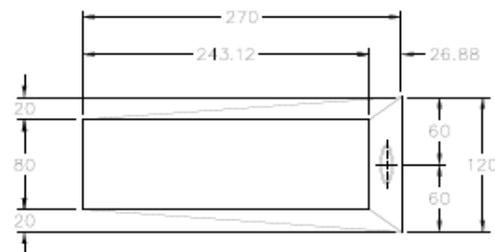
Vista E-E. Detalle geométrico de rebaje para tornillo.
